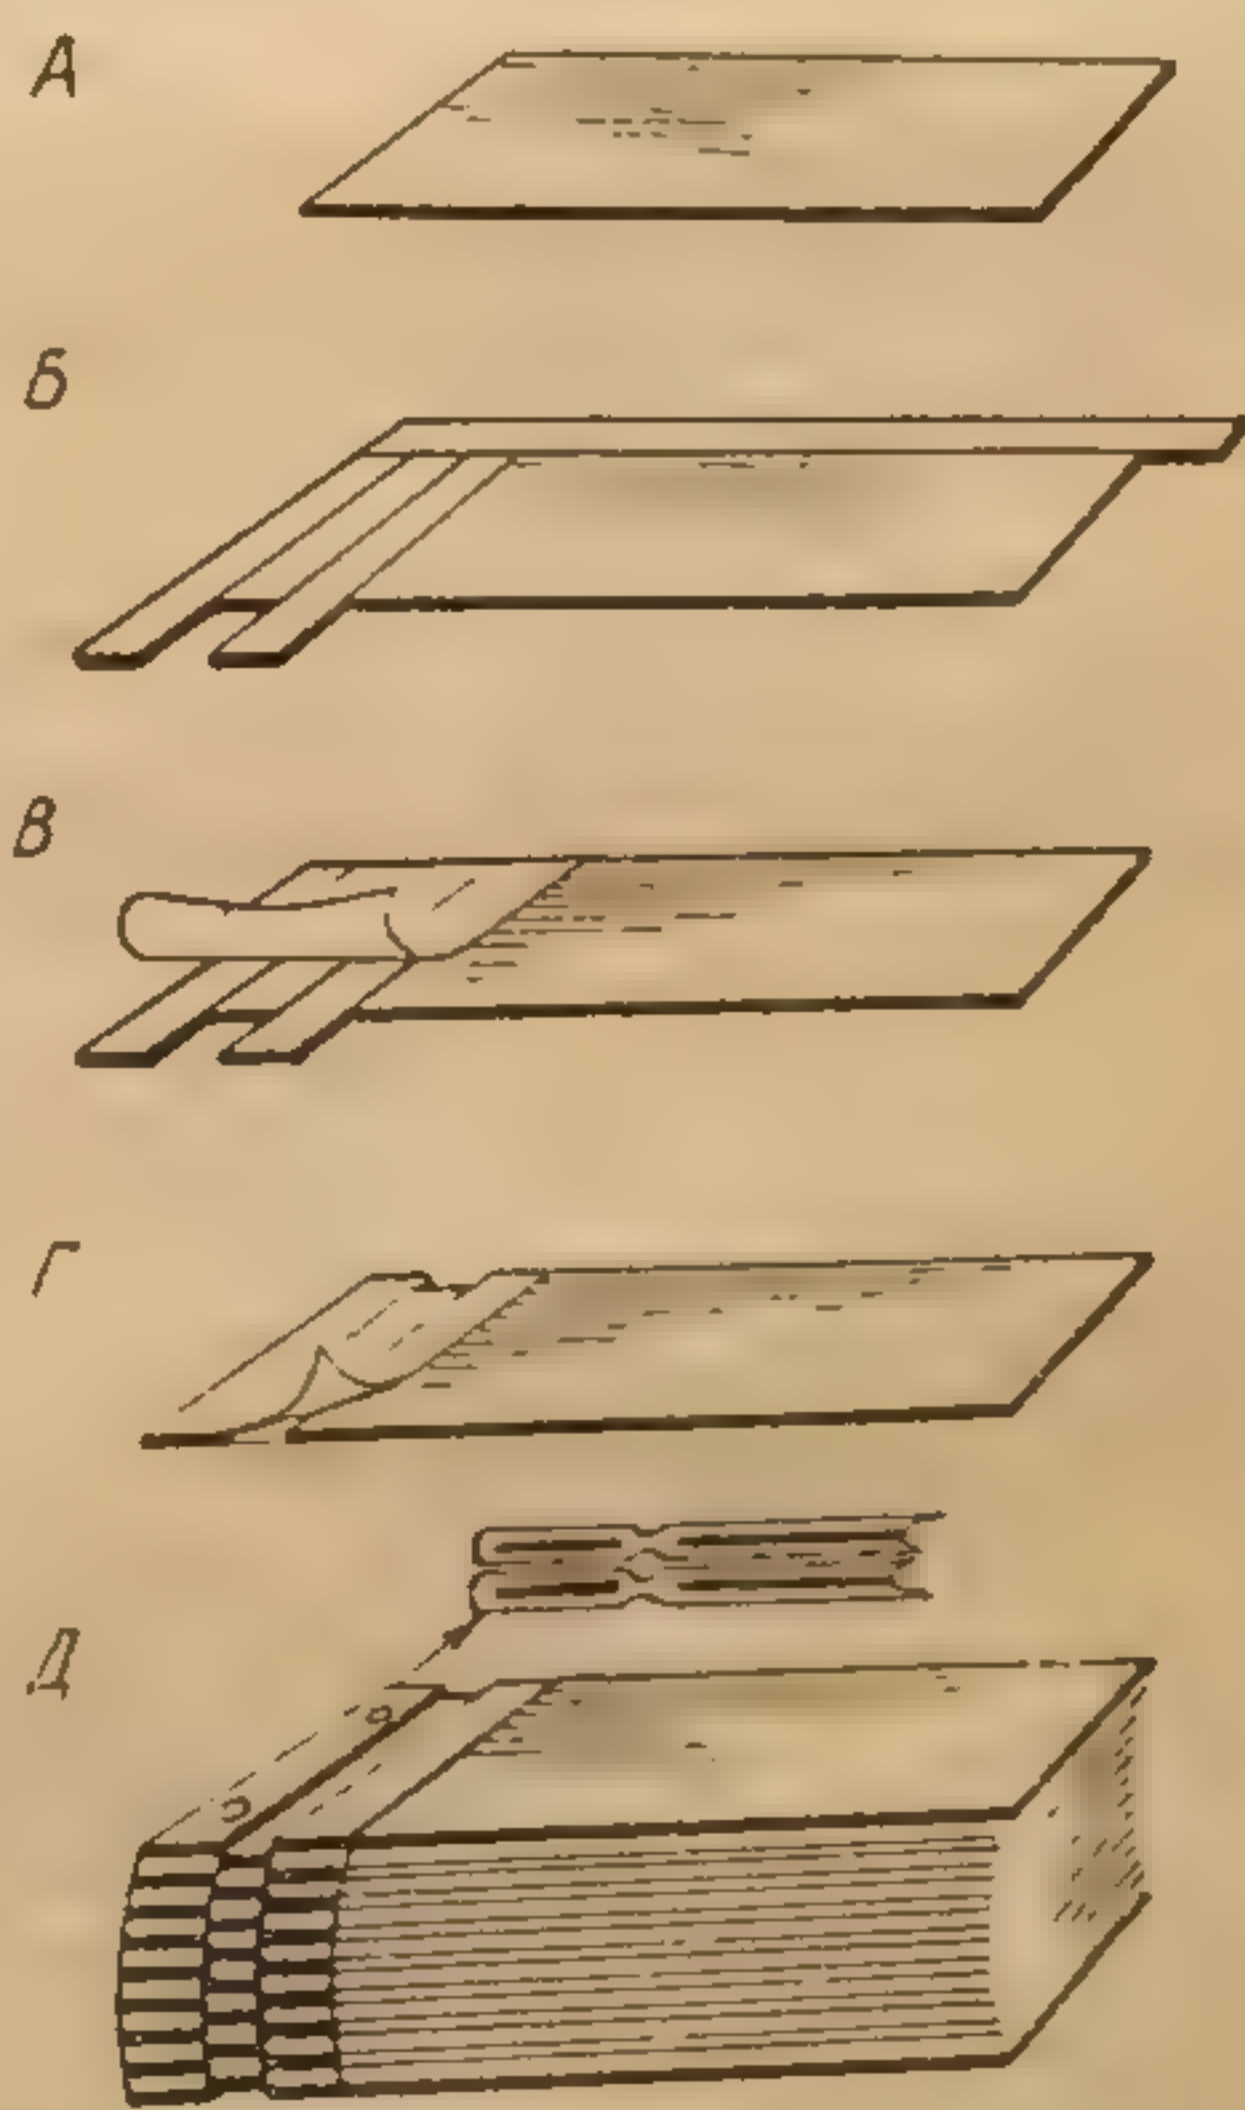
Изготовление альбомных листов с шарниром: А — картонная заготовка; Б — расположение деталей на шаблоне; В — наклейка ткани на кромку листа и шарнир; Г — оклейка тканью тыльной стороны шарнира; Д — блок в сборе
